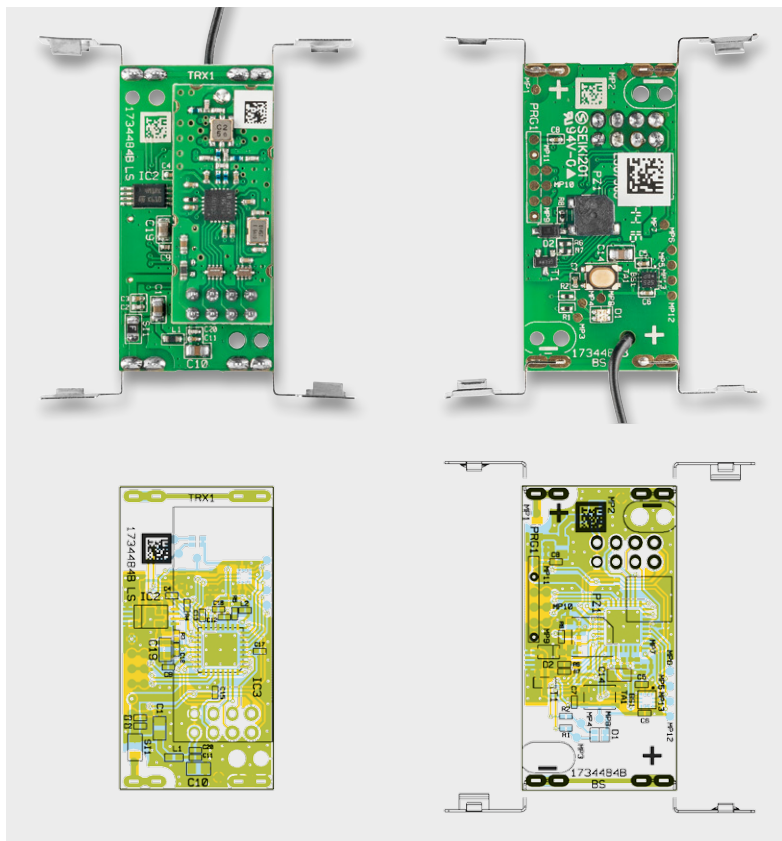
Die Platinfotos des HmIP-SAM mit der kompletten Bestückung, darunter die zugehörigen Bestückungspläne
